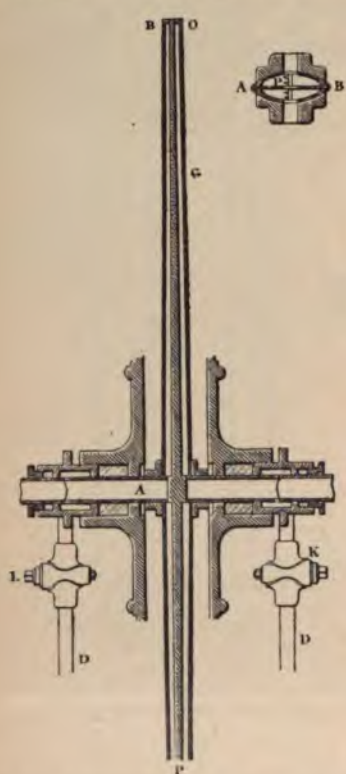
et 45. — Moteur à réaction Leroy. Coupe transversale.
